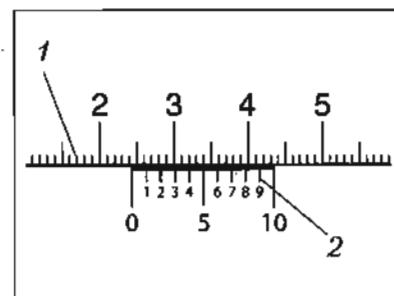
Отсчёт размера 24,3 мм штангенциркулем
